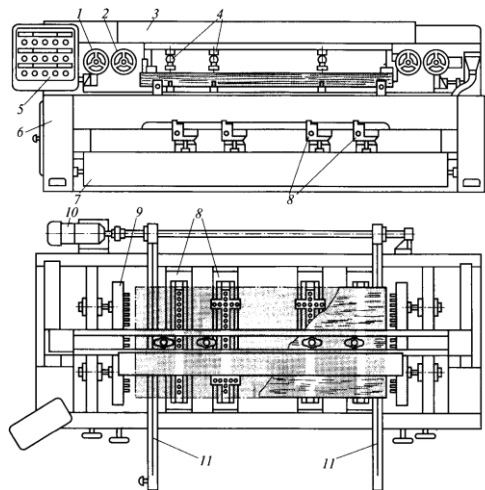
Багатошпиндельний горизонтально-вертикальний свердлильний верстат: 1, 2 – маховички; 3 – портал; 4 – притиски; 5 – пульт керування; 6 – стійка; 7 – напрямна; 8, 9 – свердлильні агрегати; 10 – мотор-редуктор; 11 – конвеєр
